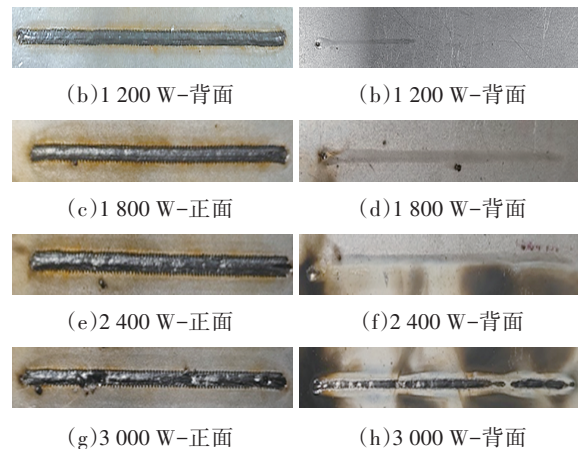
不同焊接功率下正面与背面的焊缝形貌
